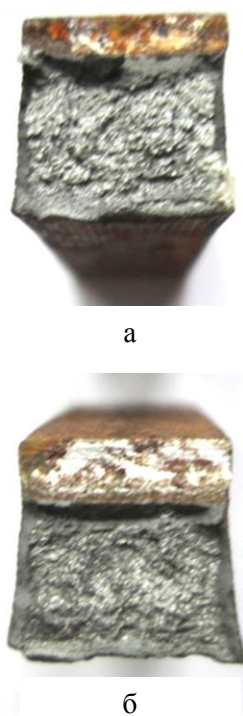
Сталь40Х холодный прокат. Изломы ударных образцов: а – безобдува, б – обдув 20 мин. Размещение образца на выходе из успокоительной камеры так, что направление обдува совпадало с направлением удара при испытании
